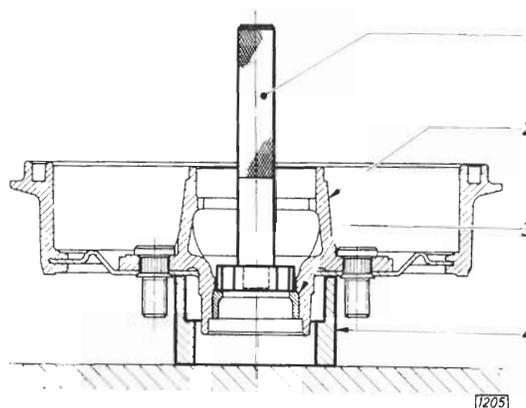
Äußeren Laufring des äußeren Radlagers herauspressen
